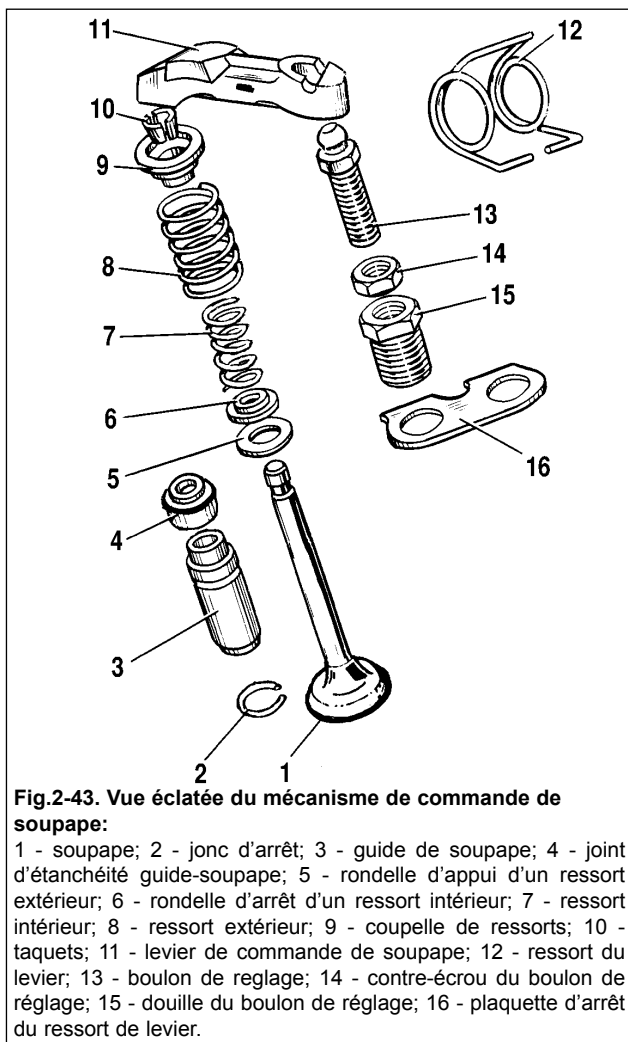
Vue éclatée du mécanisme de commande de soupape:
